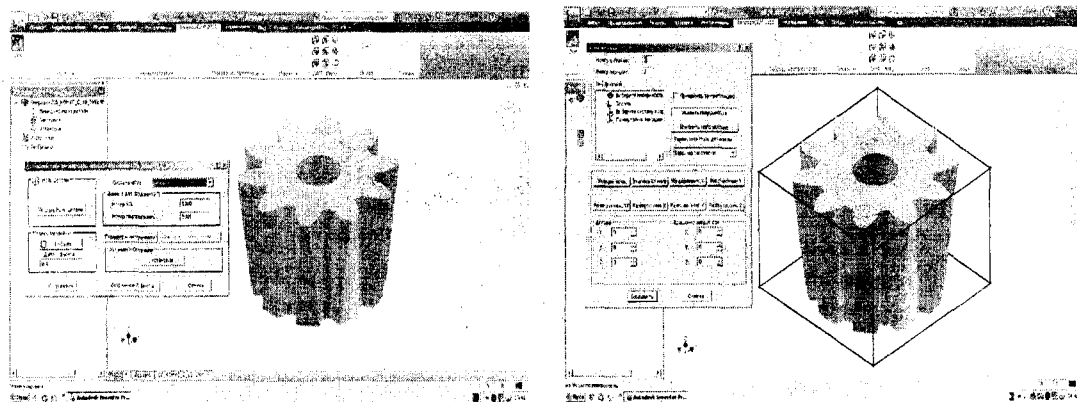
Определение геометрии заготовки и детали в InventorCAM 2011
